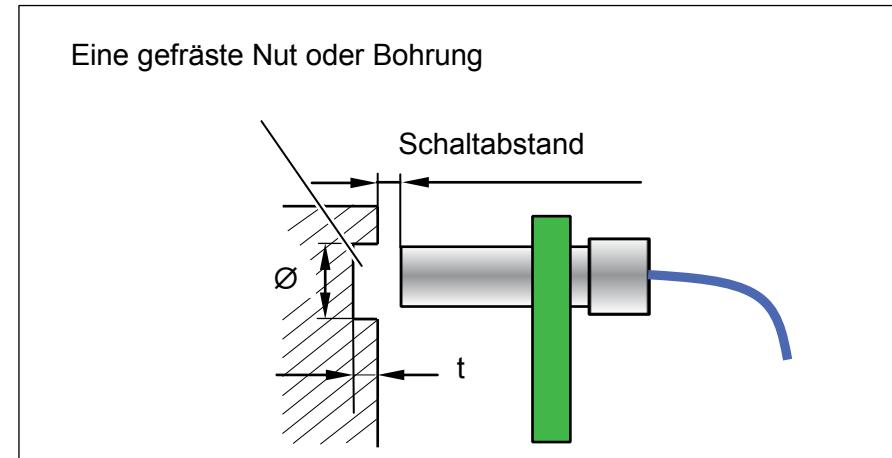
Montagebeispiel mit Nut oder Bohrung
